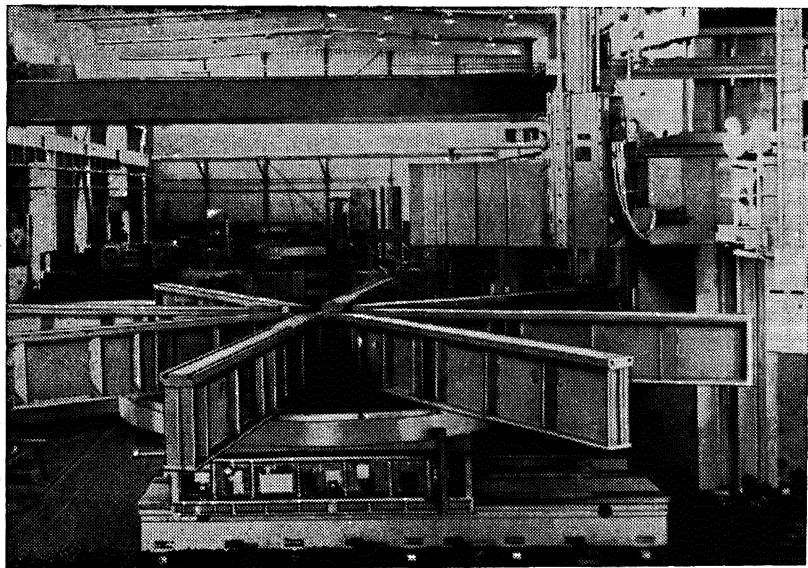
Приспособление для увеличения опорной поверхности планшайбы — опорная крестовина
